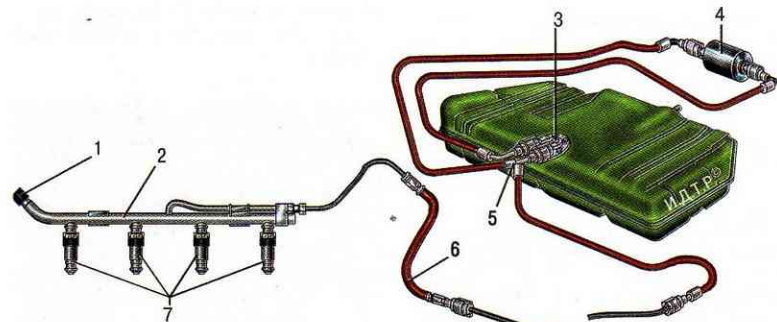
Система подачи топлива двигателей мод. 21114 и 21124: 1 — пробка штуцера для контроля давления топлива; 2 — рампа форсунок; 3 — модуль топливного насоса; 4 — топливный фильтр; 5 — тройник; 6 — подающий топливопровод; 7 — форсунки
